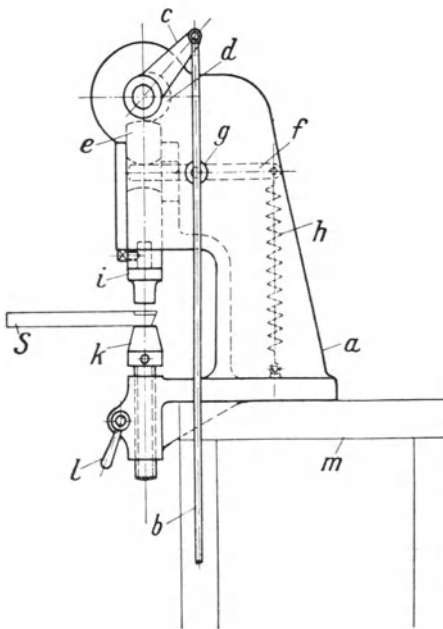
Aufschweißpresse für Edelstahlplättchen auf eiserne Halter.
